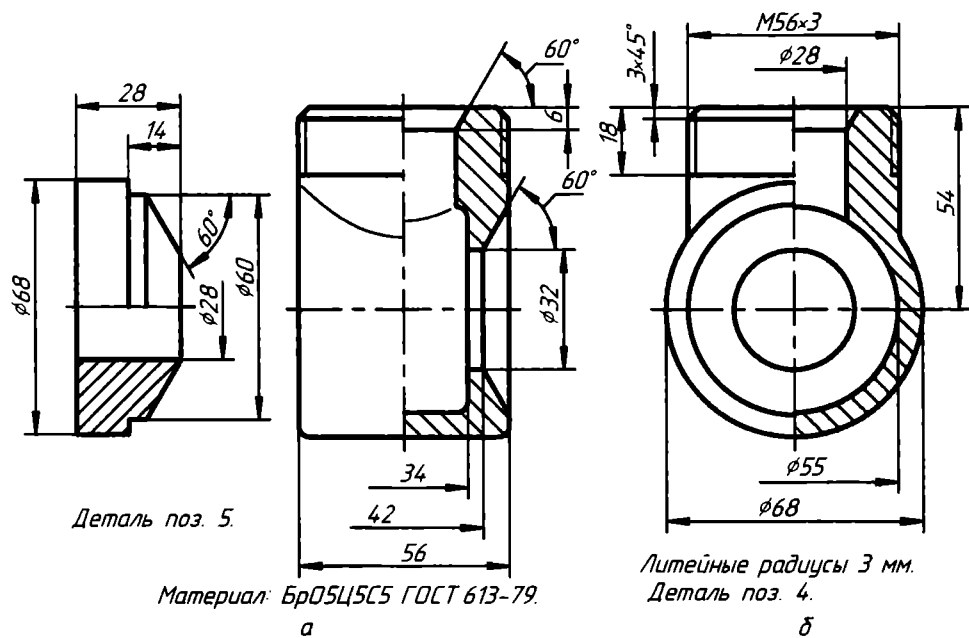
Чертежи: а — конуса; б — тройника форсунки
